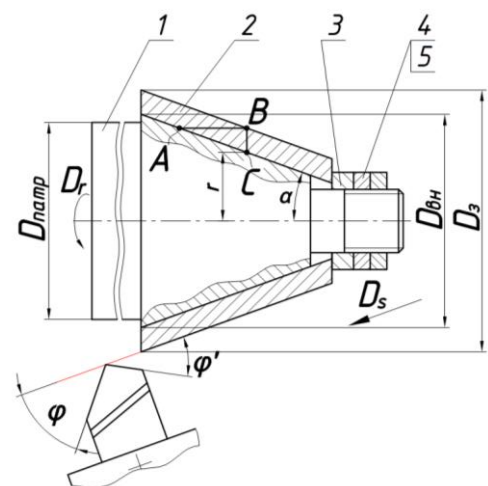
Процес обточування зовнішньої циліндричної поверхні дослідного зразка:
